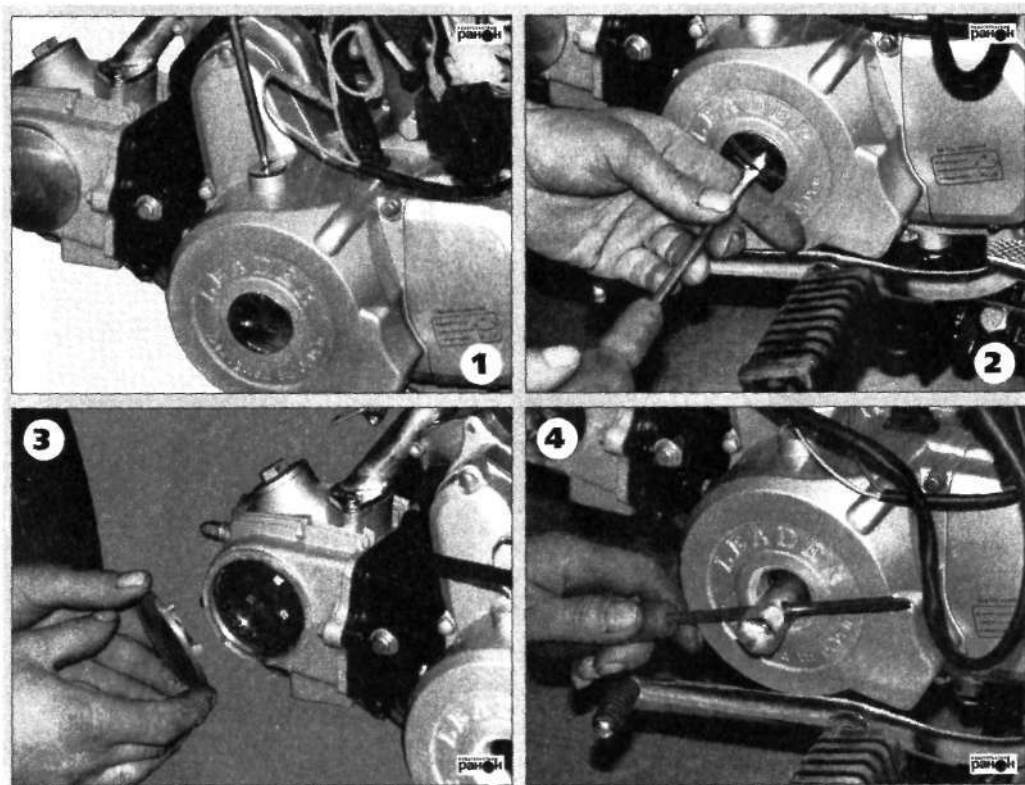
Установка верхней мертвой точки (ВМТ) конца такта сжатия
